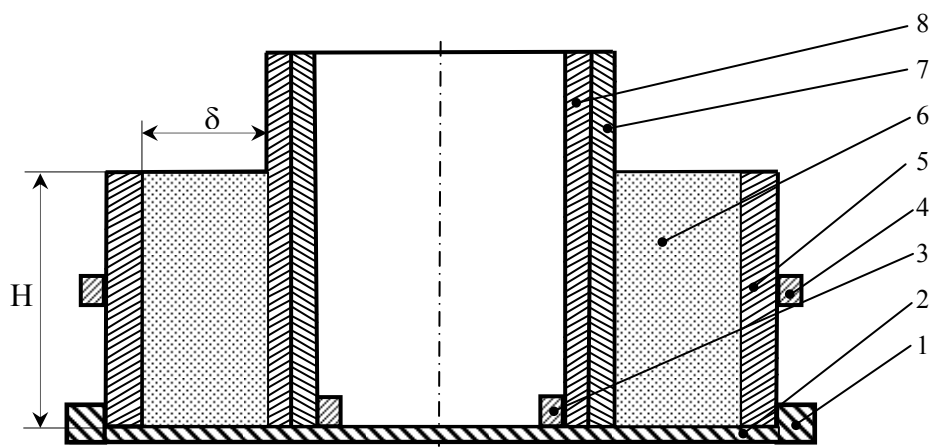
Схема форми для виготовлення КГЕ фільтру
